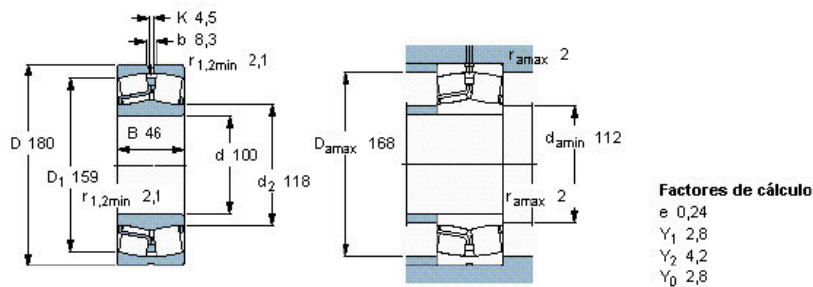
Rodamiento SKF de rodillos a rótula modelo 22220 E.
